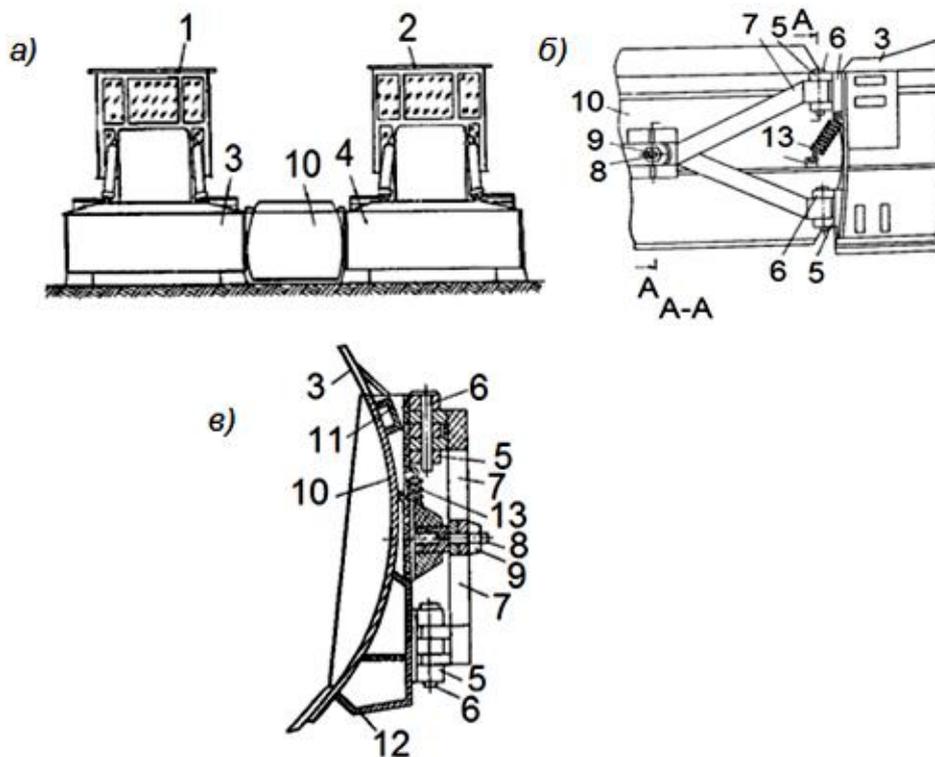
Устройство для спаренной работы бульдозеров: вид спереди (а), тоже, вид сзади (б) и разрез А-А (в): 1, 2 - базовые трактора; 3, 4 - бульдозерные отвалы; 5 - проушины; 6 - вертикальные пальцы; 7 - рычаги; 8 - горизонтальная ось; 9 - гайка; 10 - плита; 11, 12 - коробки жесткости; 13 - пружины
